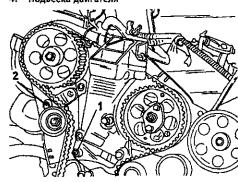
Гайка (1) и болт (2) крепят натяжной ролик автоматического натяжного устройства зубчатого ремня.
